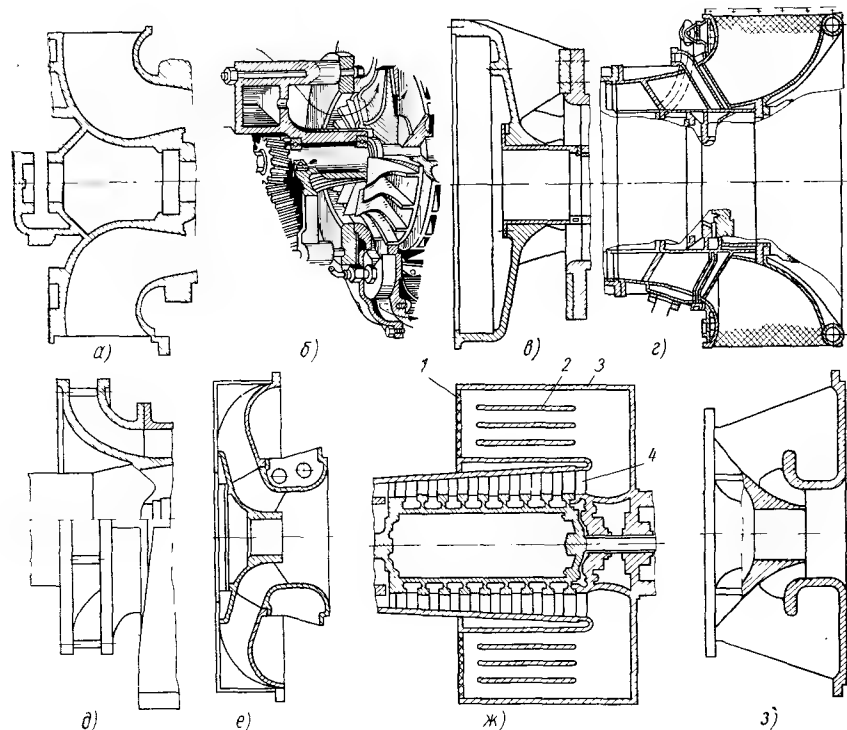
Входные патрубки компрессоров с кольцевым подводом ГТУ:
